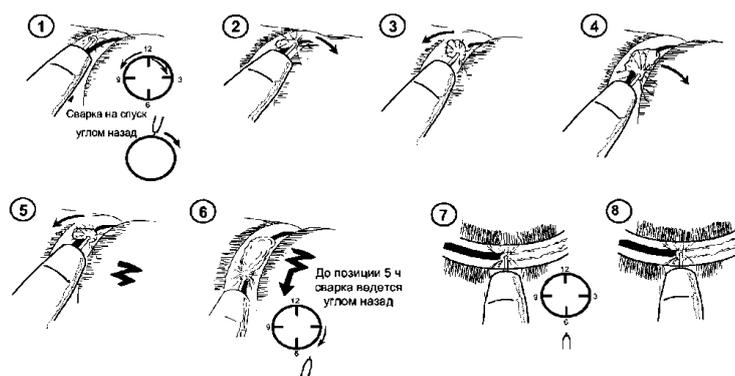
Техника сварки корневого шва неповоротных стыков трубопроводов методом STT [1]
